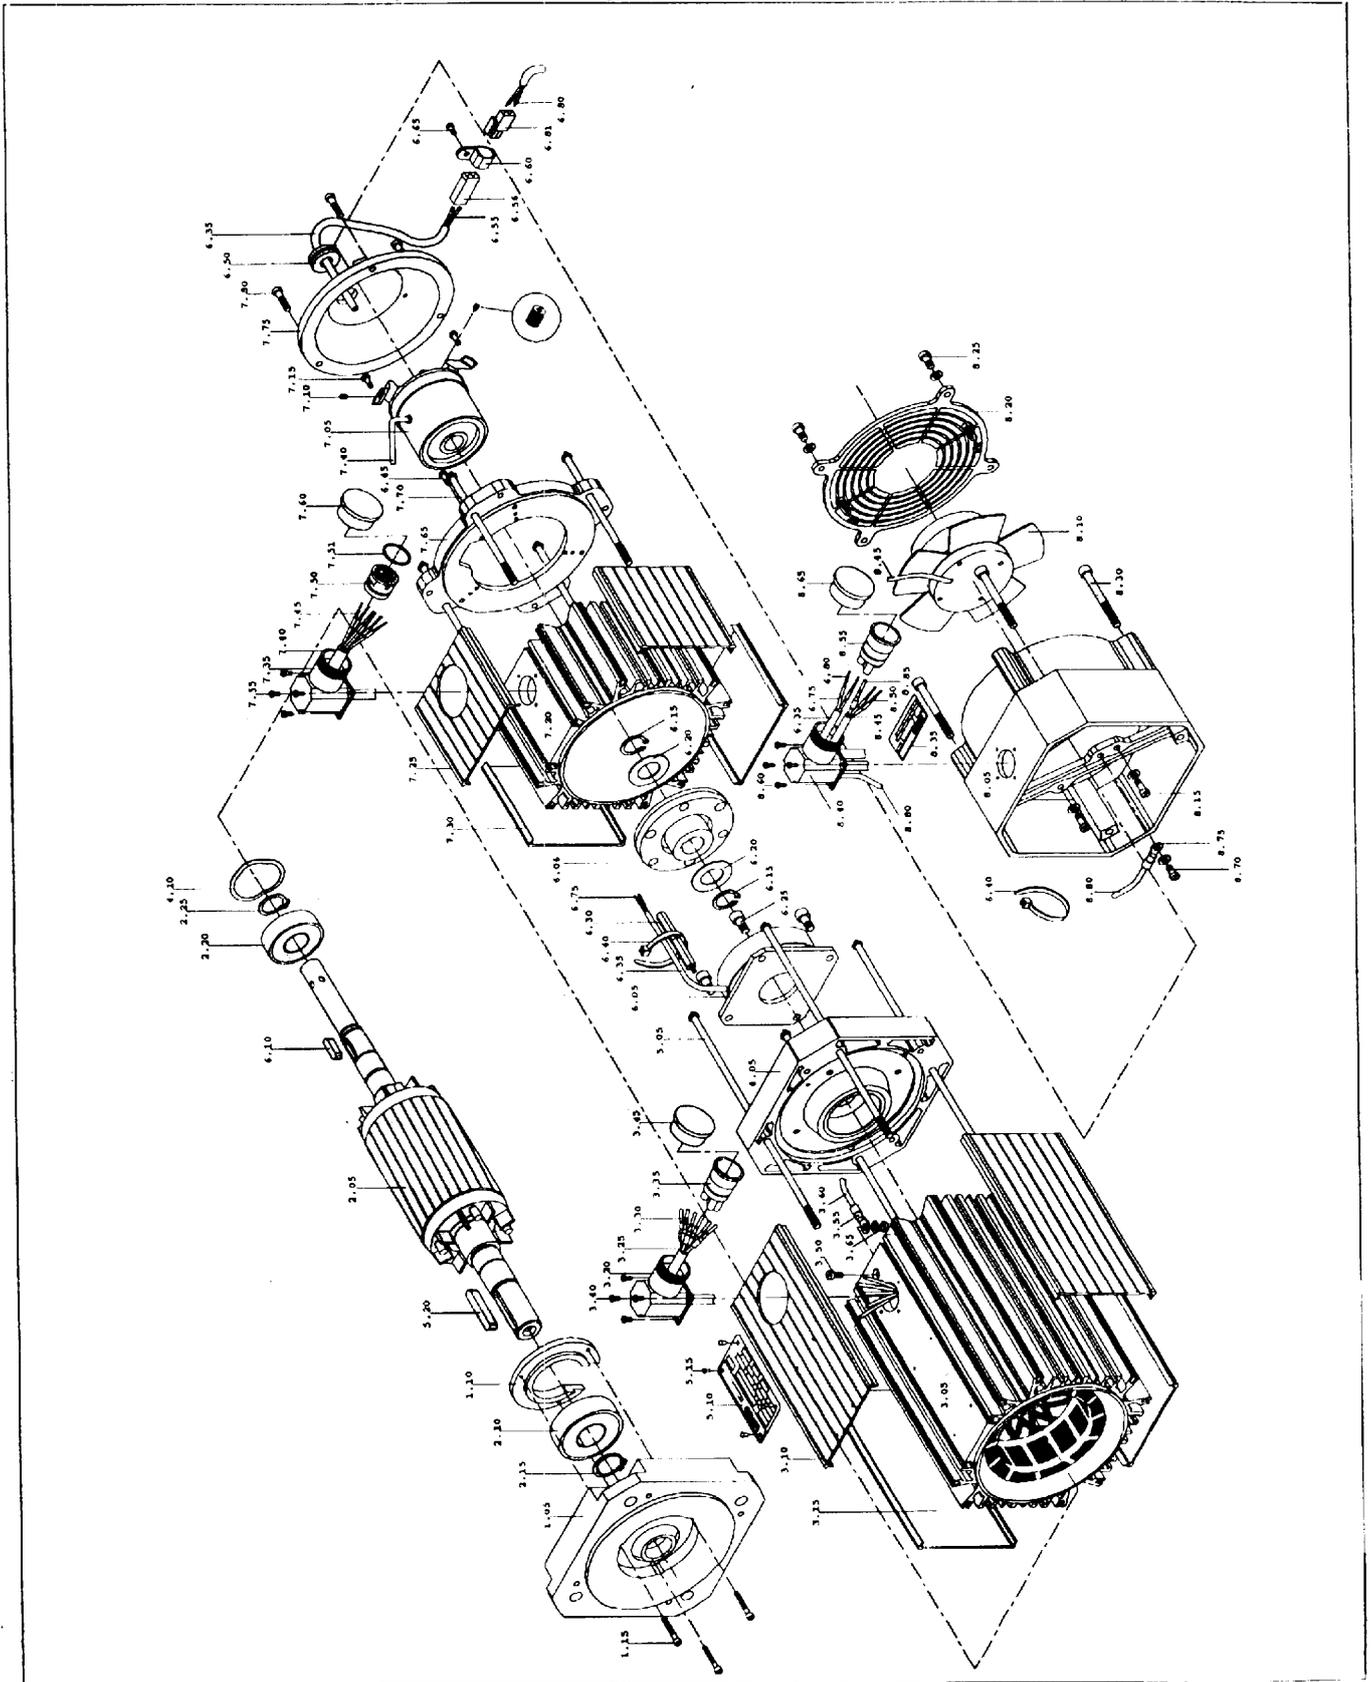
Explosionszeichnung Motor mit Bremse und Lüfter DFVABS
